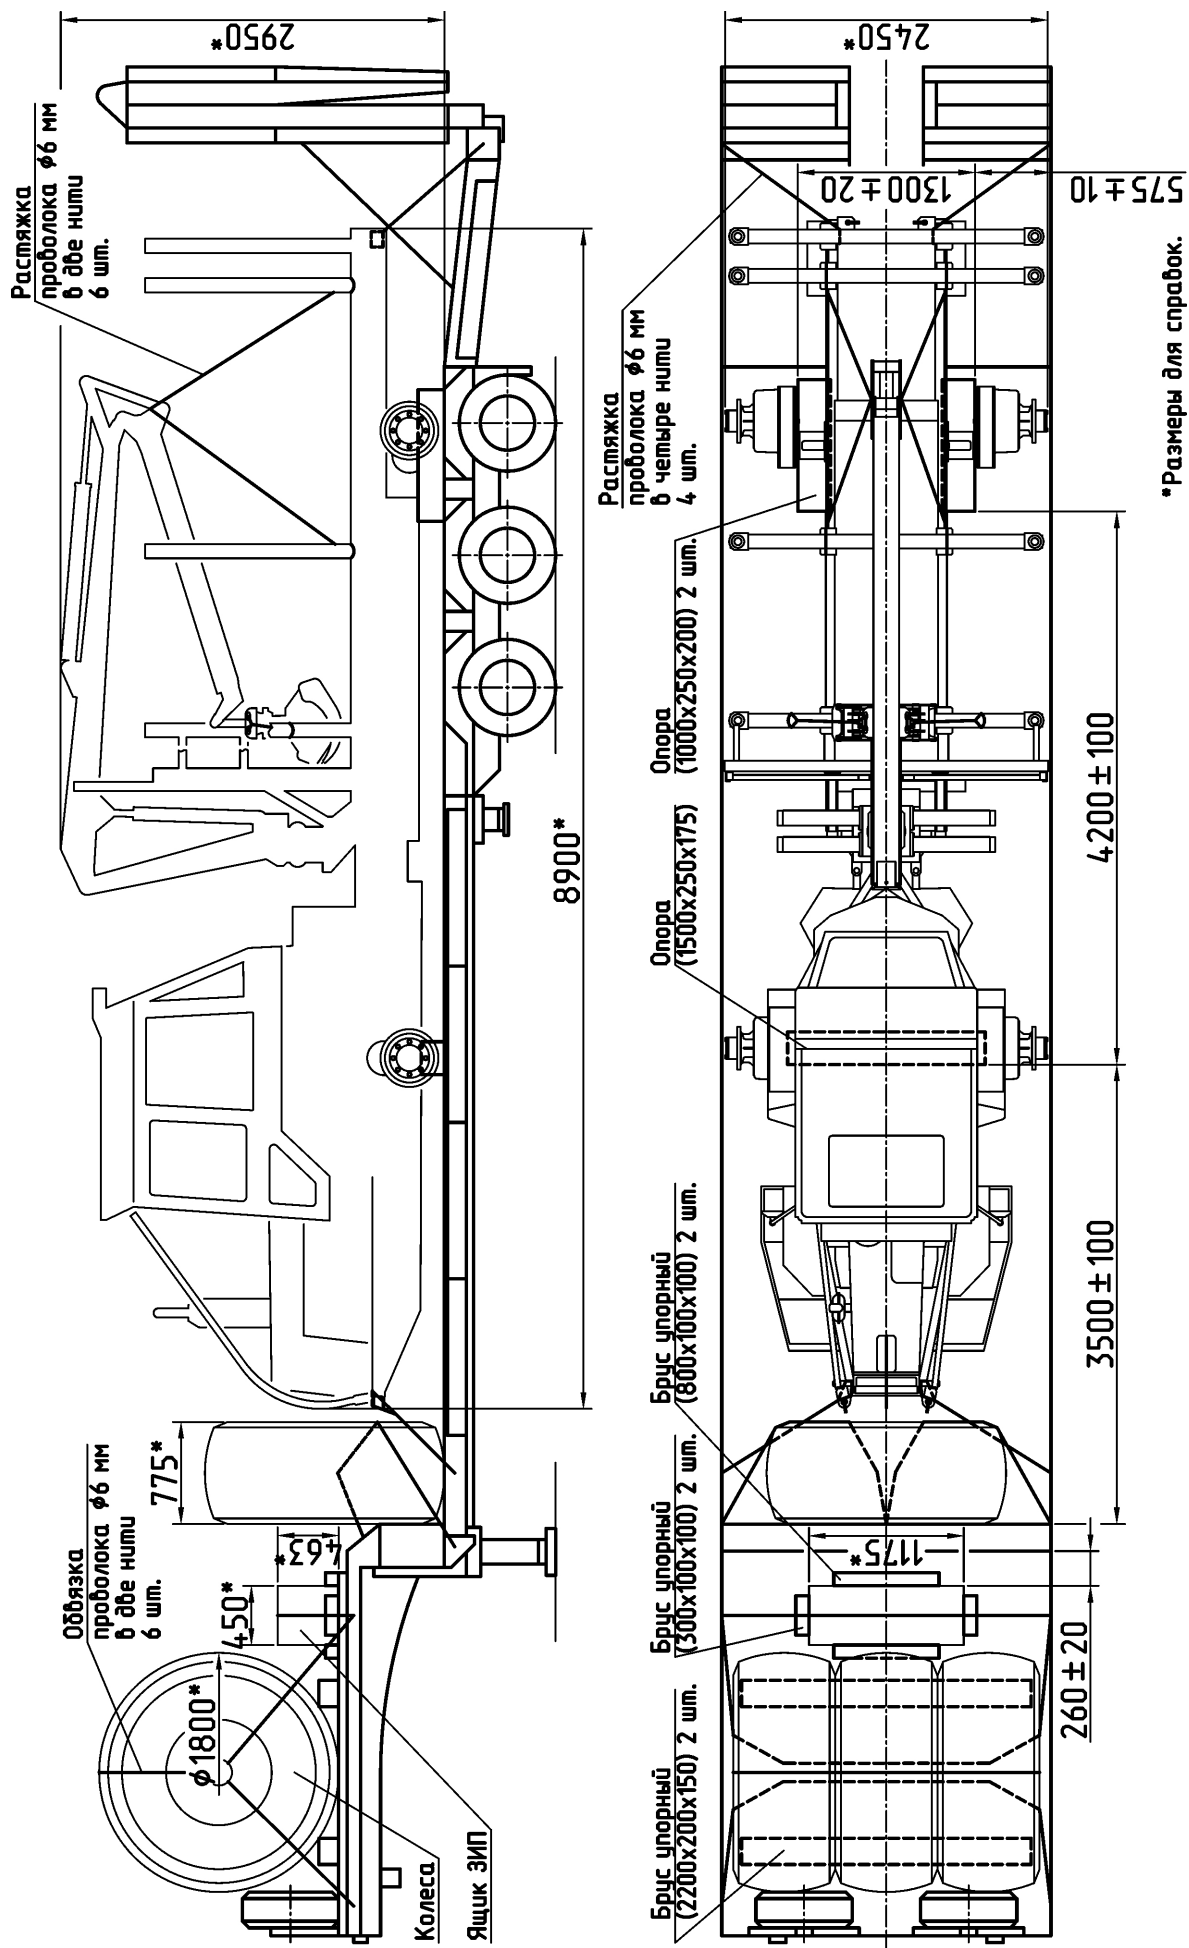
Схема установки и крепления машины на полуприцепе 9338-0000010-01
